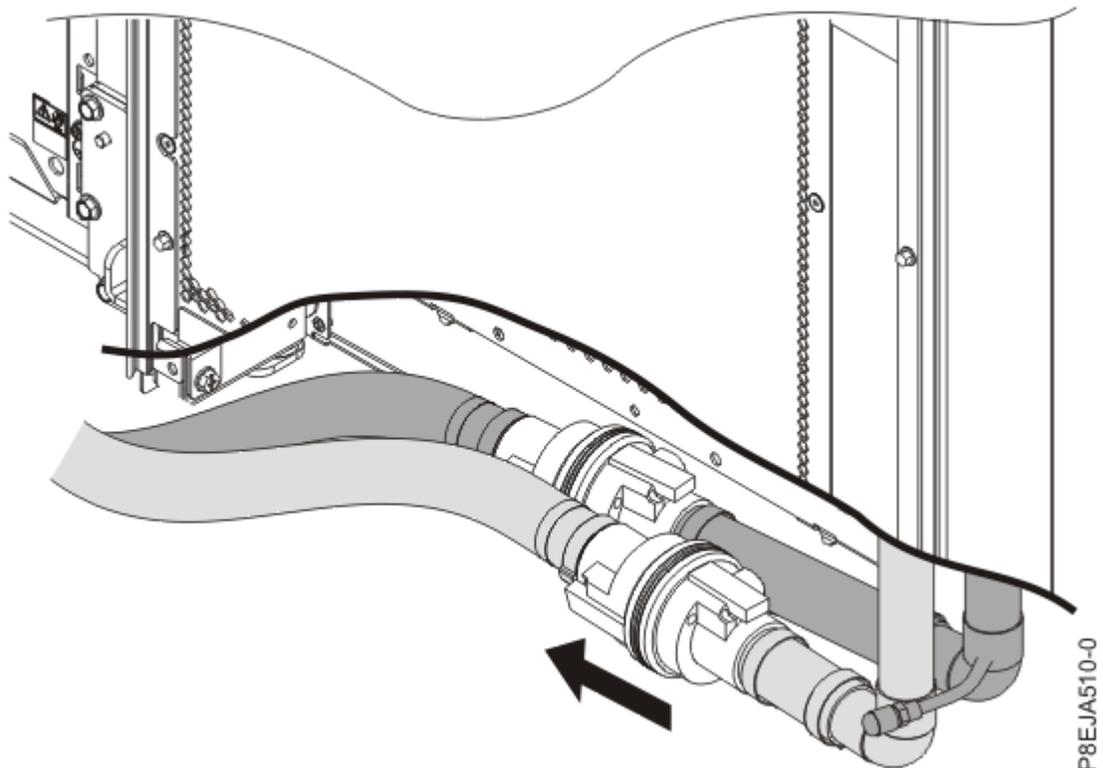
Flexible Schläuche, die an der Unterseite des Rear Door Heat eXchanger befestigt sind
